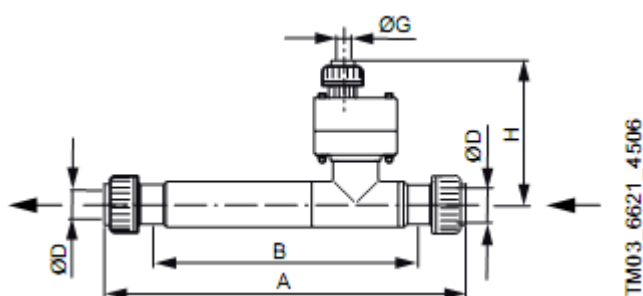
Габаритный чертеж, инжекторы 20-40 кг/ч
